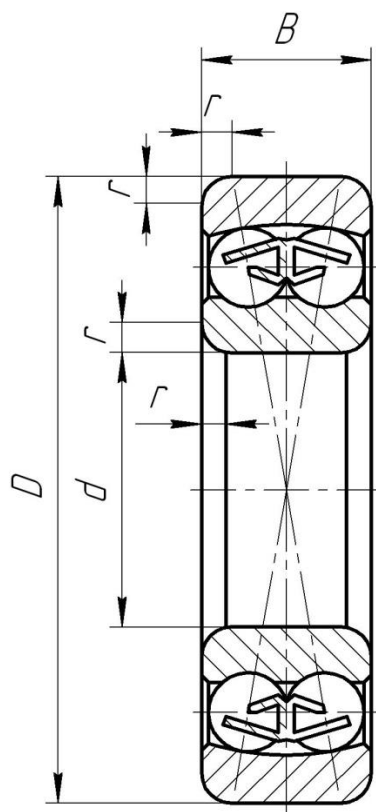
Подшипник радиальный сферический, двухрядный
